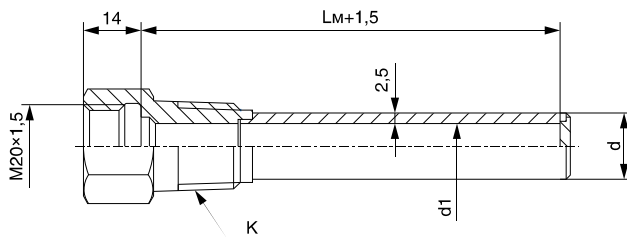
ГТ-701 с конической резьбой для ДТ с подвижным штуцером
